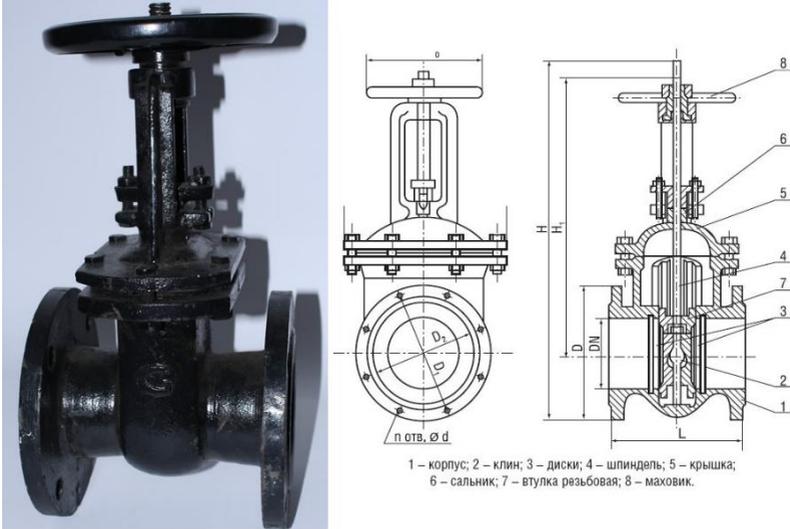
Задвижка параллельная 2-х дисковая: 1- корпус; 2- распорный клин; 3- уплотнительные кольца; 4-шток; 5- крышка; 6- сальник; 7- диски; 8- маховик
